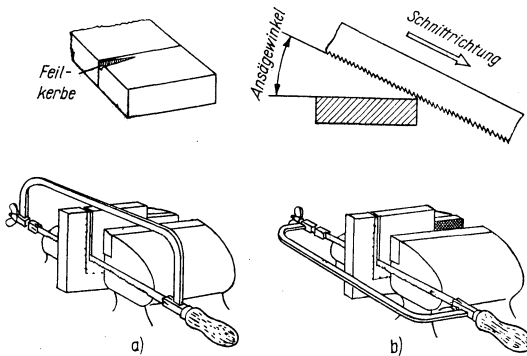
Zum besseren Anschnitt der Säge wird mit der Feile angekerbt (links); die Säge wird mit einem bestimmten Winkel angesetzt (rechts oben); ist der Sägeschnitt zu lang (a), dann wird das Sägeblatt umgespannt (b)
